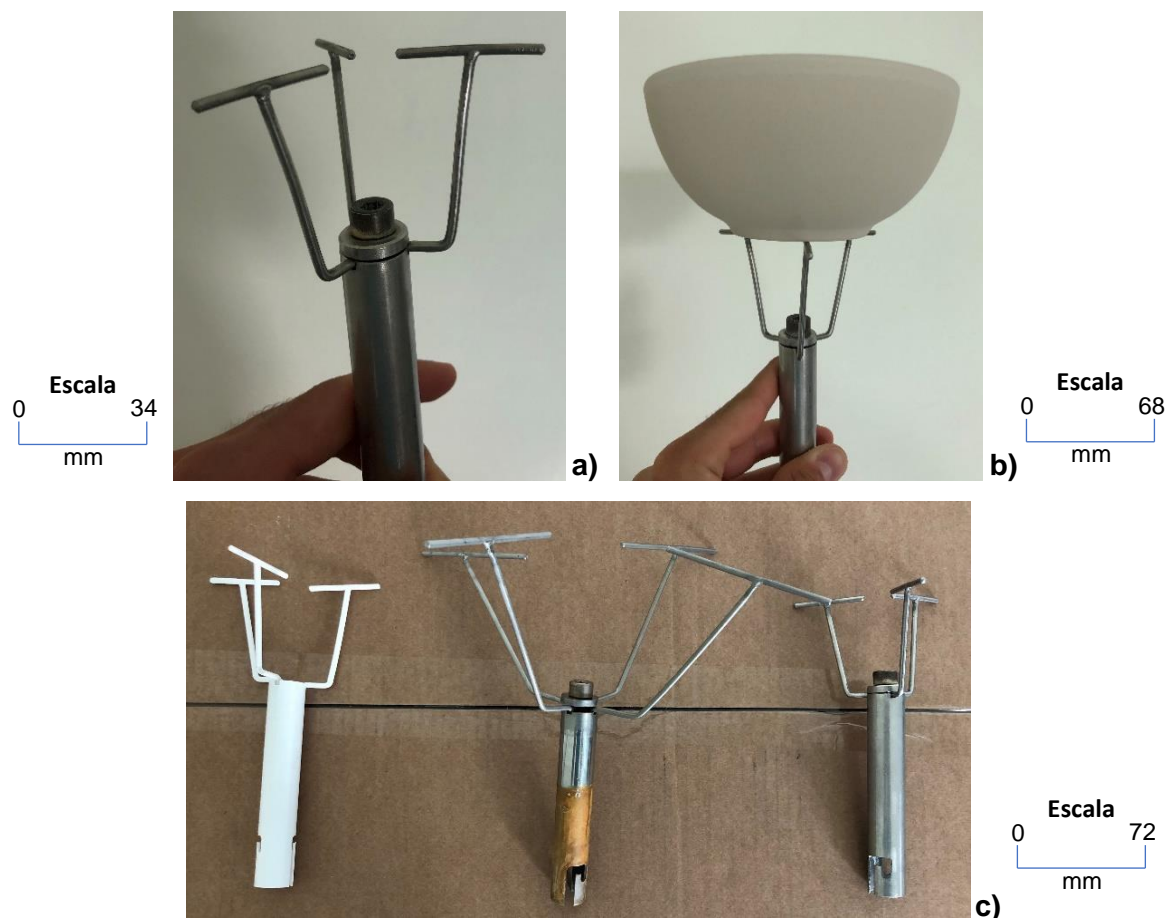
Spindle de dimensão *S*: a) produzido; b) produzido e com uma peça com pequenas dimensões e c) comparação entre os spindles de dimensão *M* antes da otimização e de dimensão *S* produzido para testes em impressão 3D e em AISI 302.
